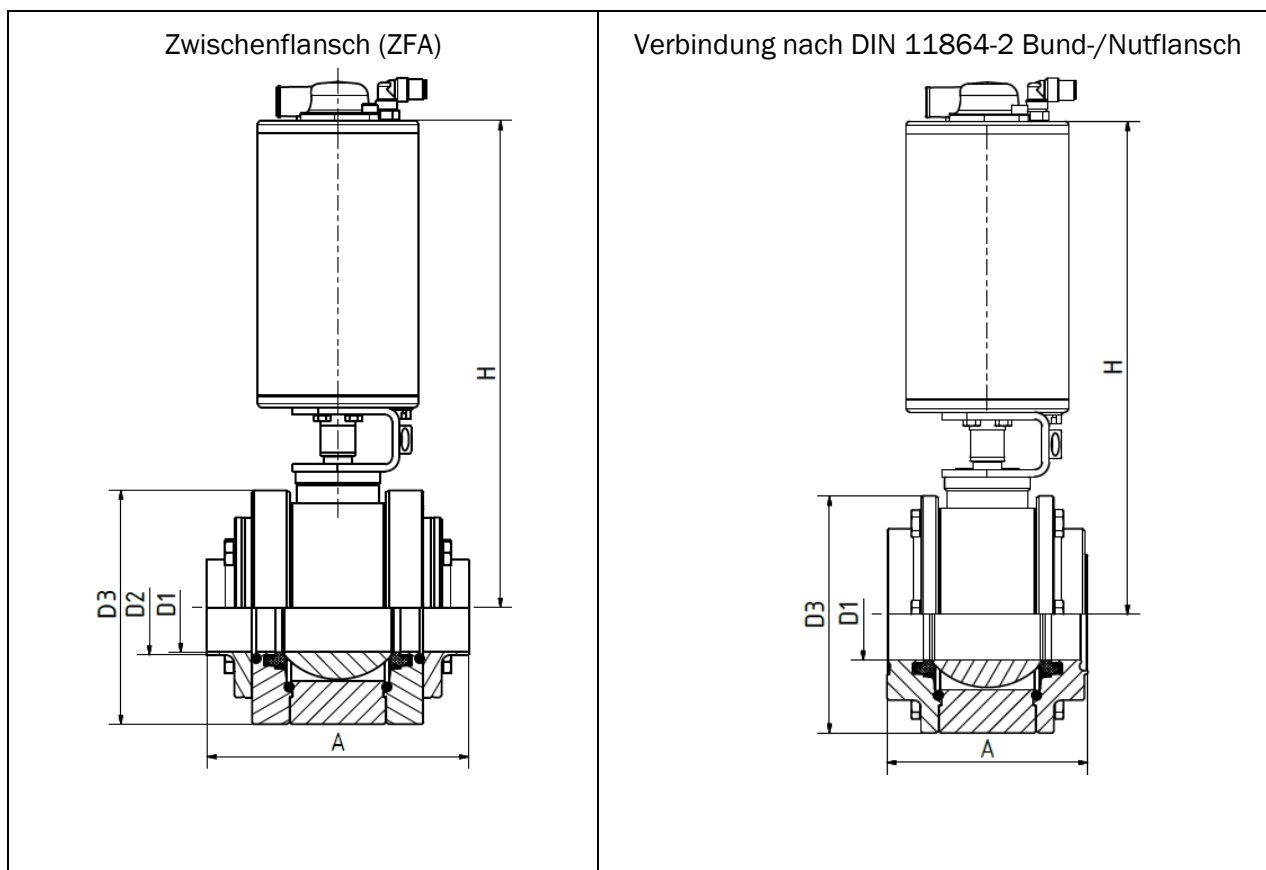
Kugelventil mit pneum. Antrieb: Anschlussvariante ZFA, DIN 11864-2
